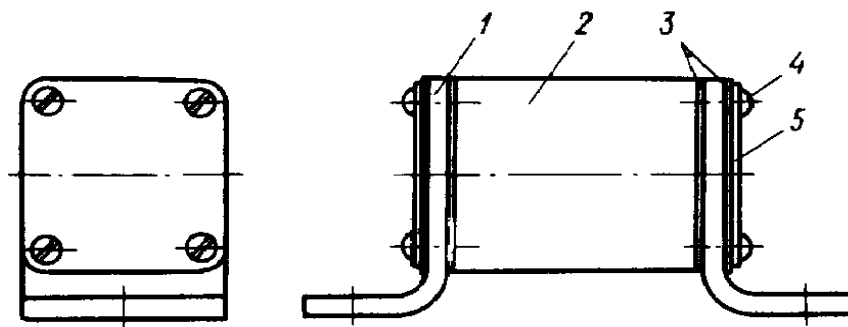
Загальний вид швидкодіючого запобіжника
